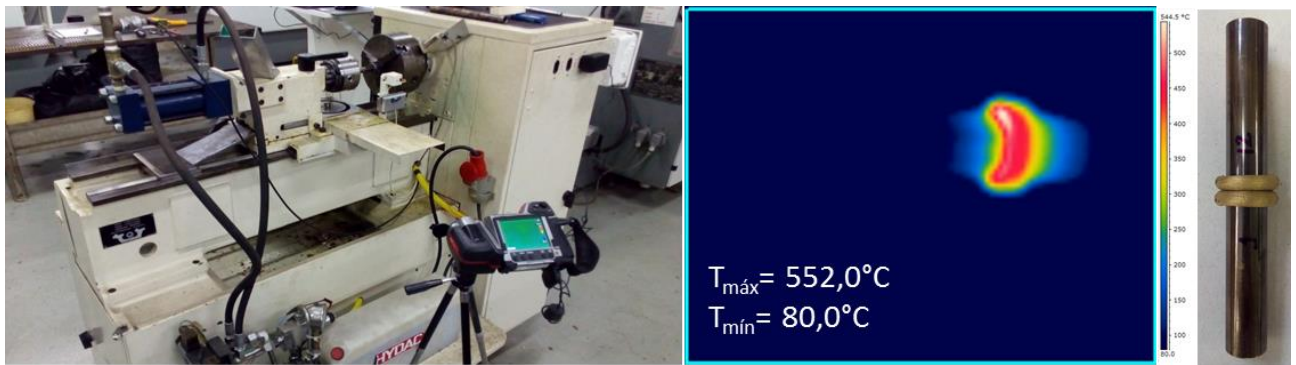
a) equipamento de soldagem (esquerda) b) termograma do processo de soldagem (centro) c) junta unida pelo processo de soldagem por atrito convencional (direita) (Do Autor)
